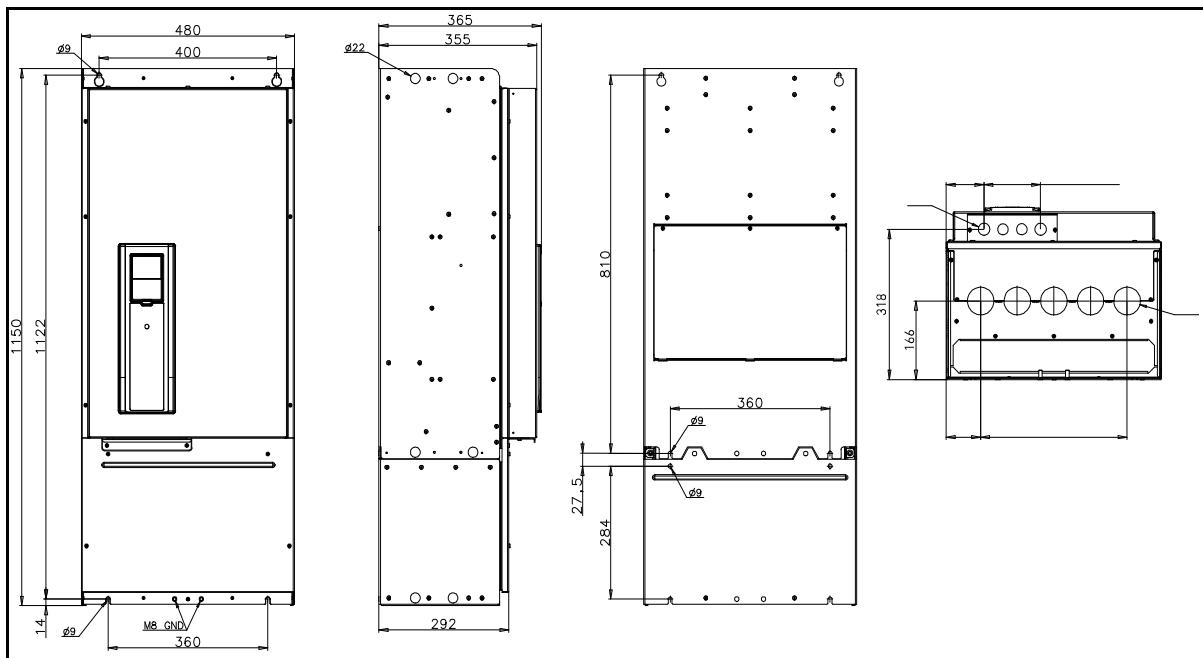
Размеры привода переменного тока Vacon, типоразмер MR9, классы защиты IP21 и IP54
